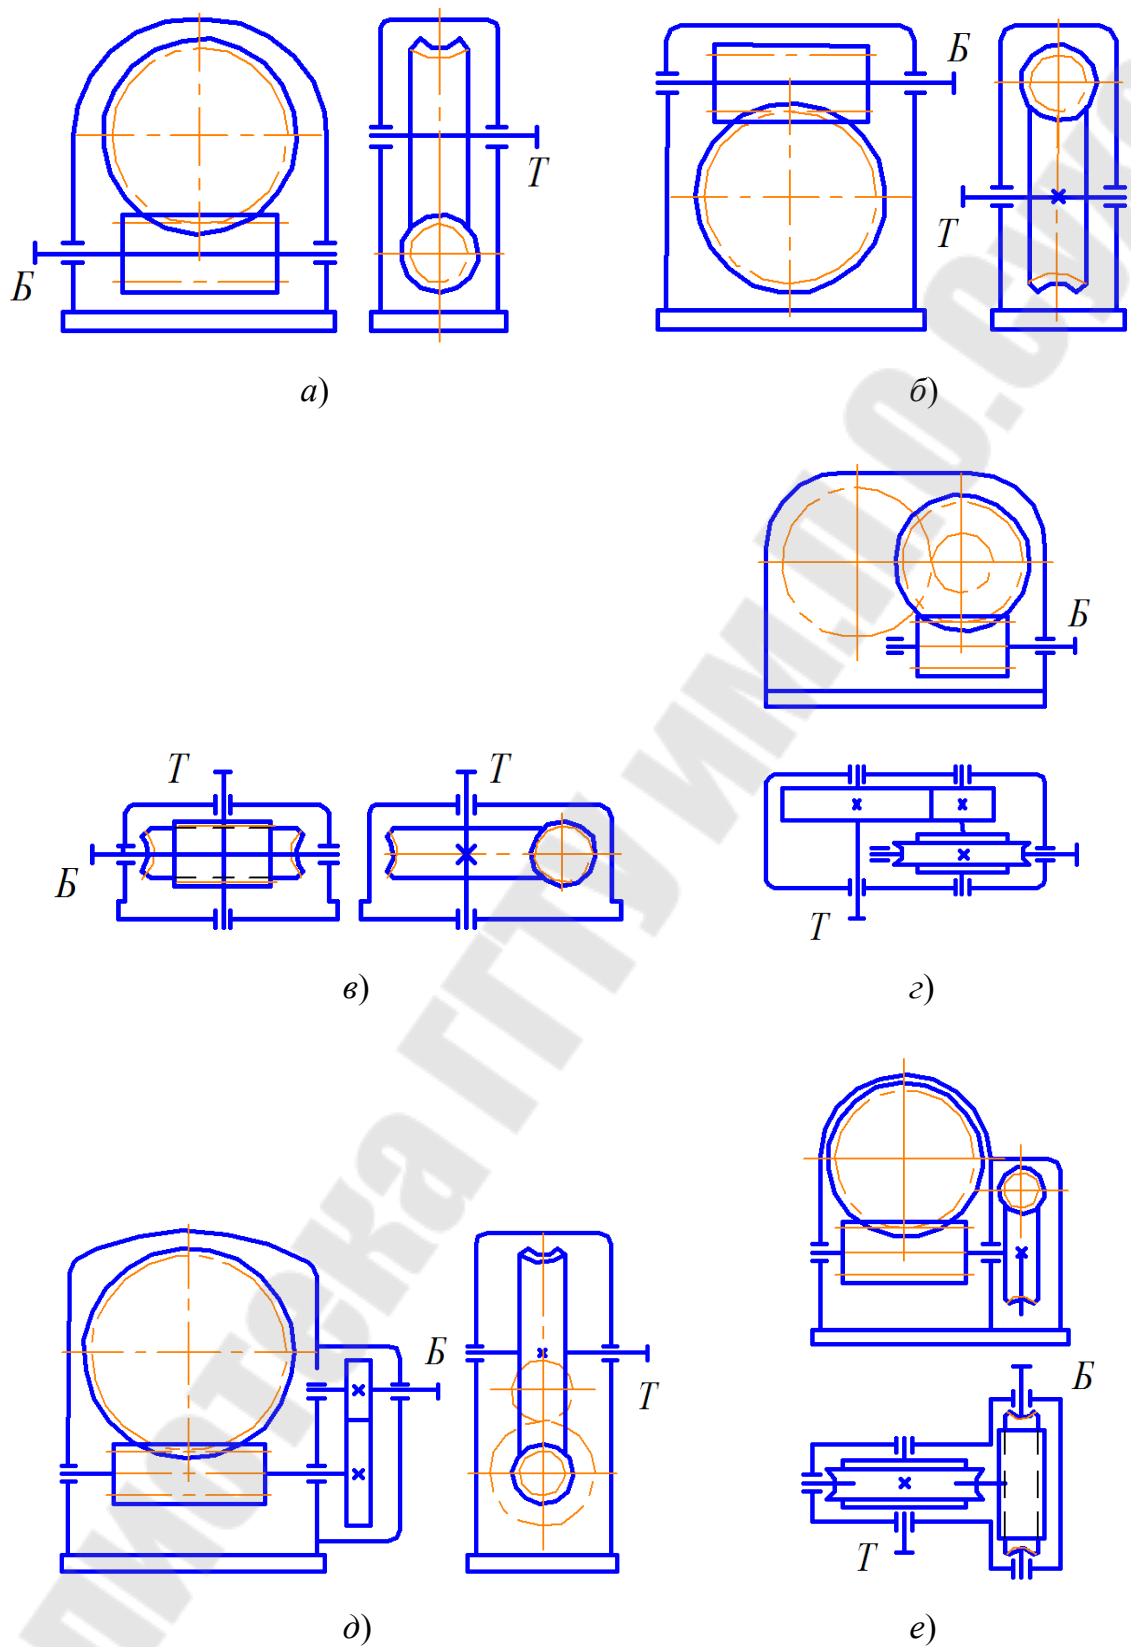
Кинематические схемы червячных и зубчато-червячных редукторов
